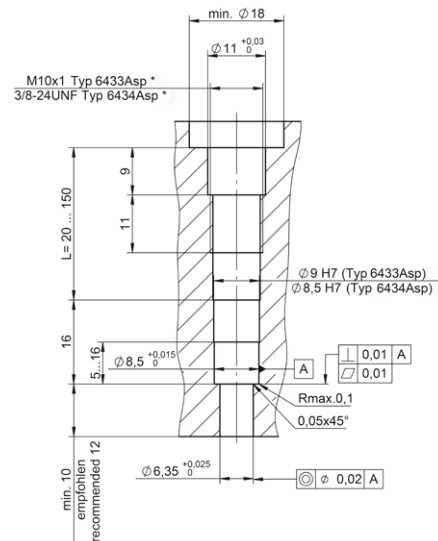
Bohrung für Einbau mit Montagehülse, kundenspezifisch
